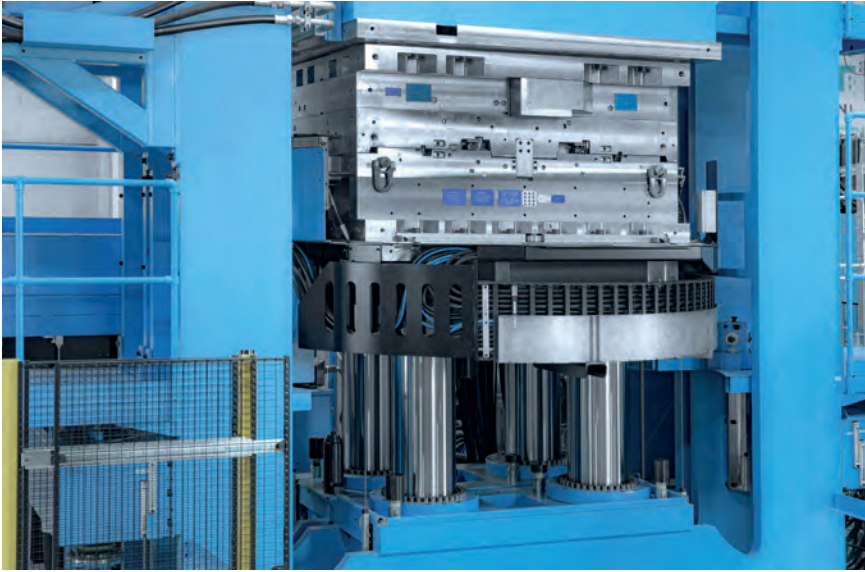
Detailansicht des Drehtisches mit dem 18 t schweren Spritzgießwerkzeug und den vier Druckkissenmodulen © LWB Steintl
